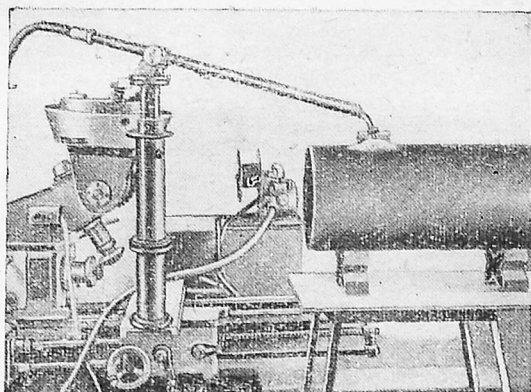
Сварка прямого шва под слоем флюса на сварочном станке.
